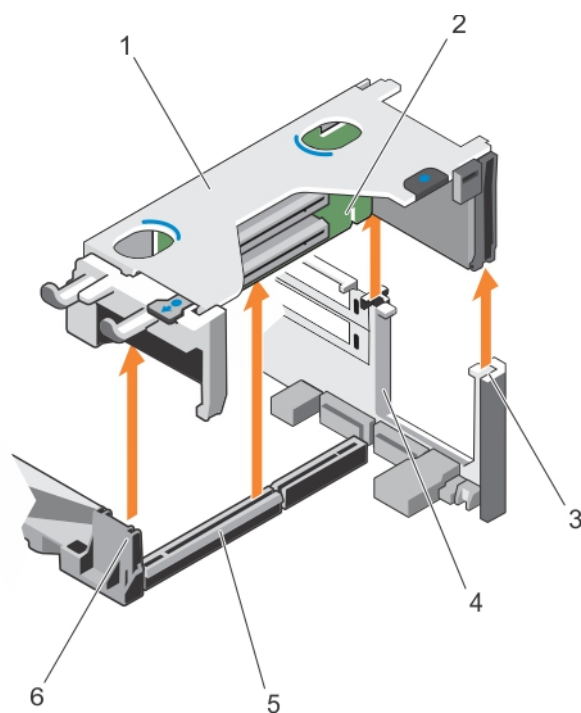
Rimozione e installazione del montaggio 1 della scheda di espansione
